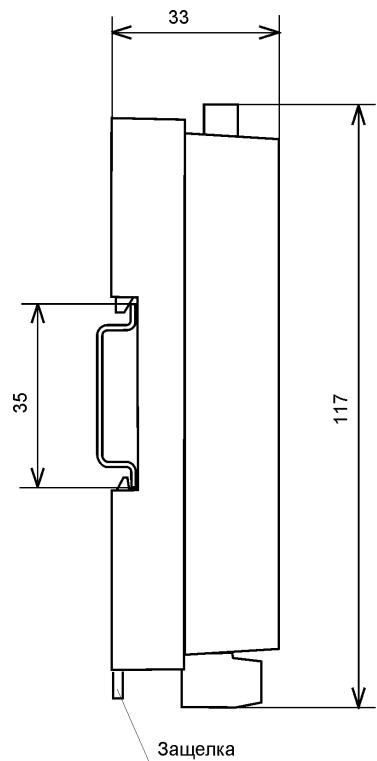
Габаритный чертеж модуля с креплением к DIN-рейке. Вид сбоку.
